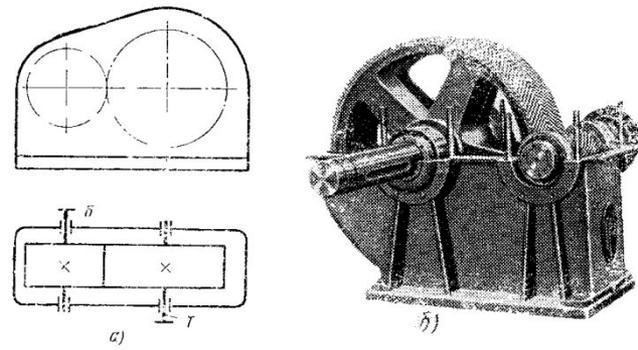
Одноступенчатый горизонтальный редуктор с цилиндрическими зубчатыми колесами:
